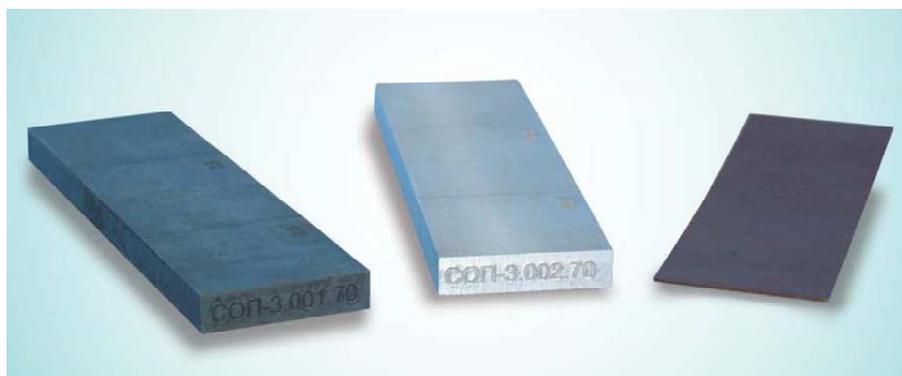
Общий вид образцов СОП-Д.М и СОП-Т.Н
